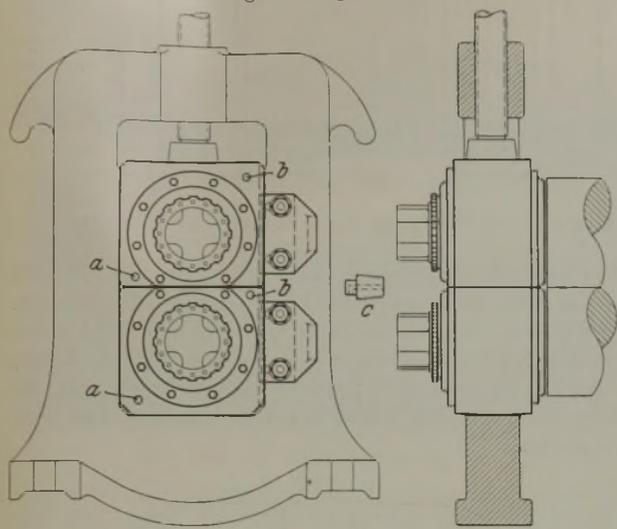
Duowalzengerüst mit Kegelrollenlagern.
